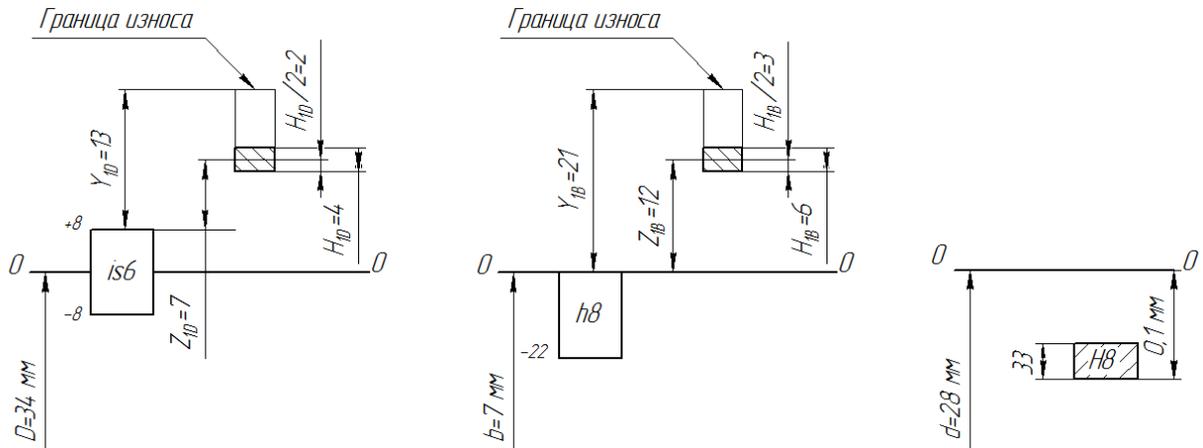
Схема полей допусков комплексного шлицевого калибра-кольца
